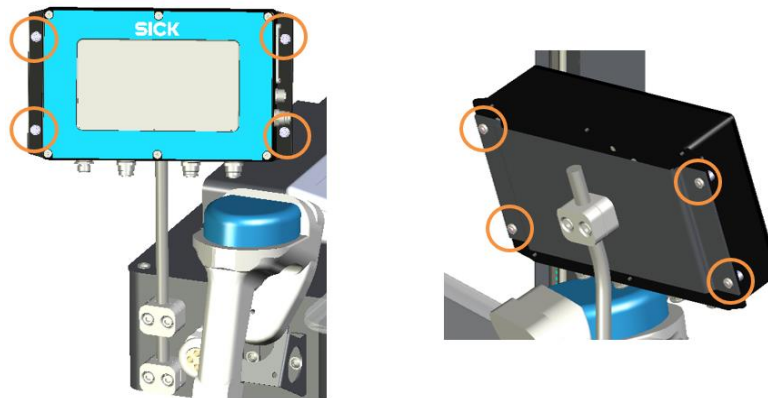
Remplacement de composants - Afficheur (démontage/montage)
